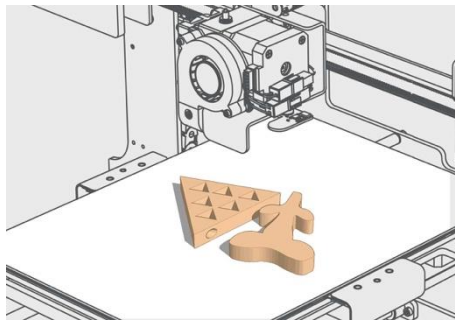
Las Dimensiones de la Pieza Están Limitadas a las Dimensiones de la Base
